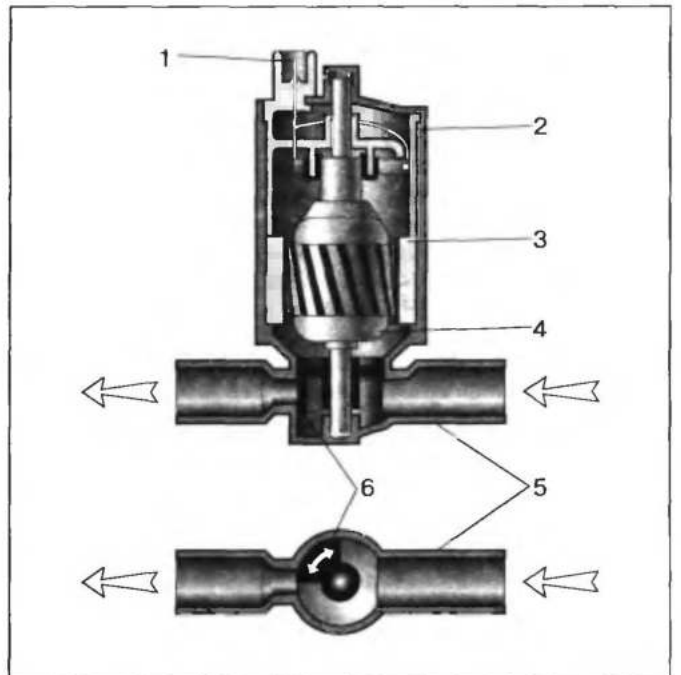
Конструкция регулятора холостого хода фирмы BOSCH: 1 — электрический контакт разъема; 2 — корпус; 3 — постоянный магнит; 4 — якорь; 5 — воздушный канал; 6 — регулирующая заслонка-сегмент
